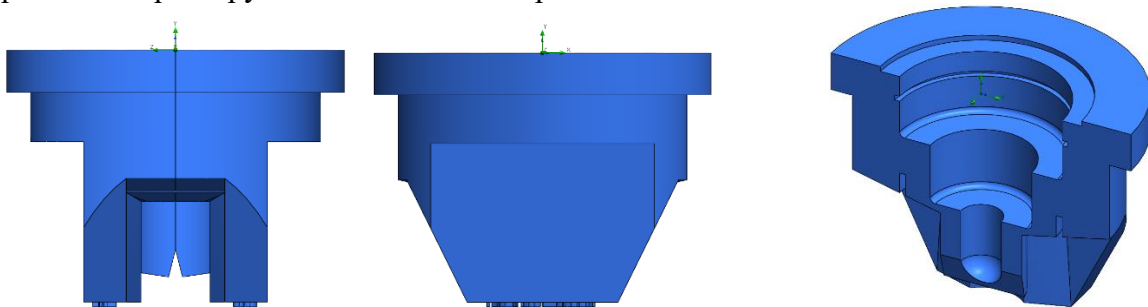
Твердотільна модель стандартного щілинного розпилювача типу 110-03
